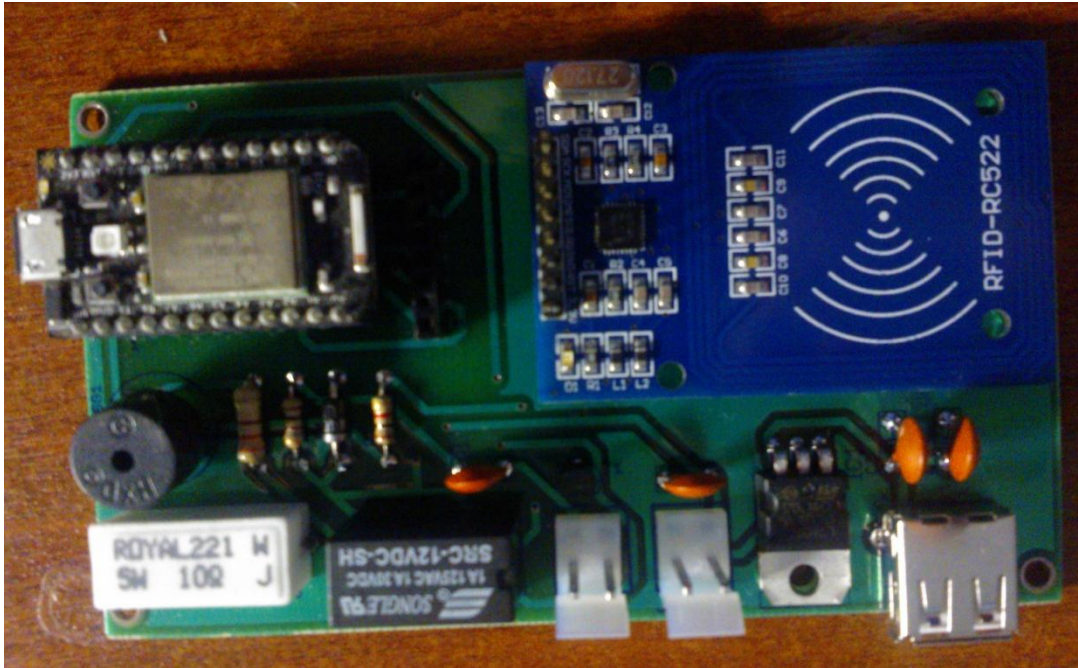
PCB IMPLEMENTADO A DOBLE CAPA CON ELEMENTOS POSICIONADOS Y SOLDADOS. FUENTE: EL AUTOR
